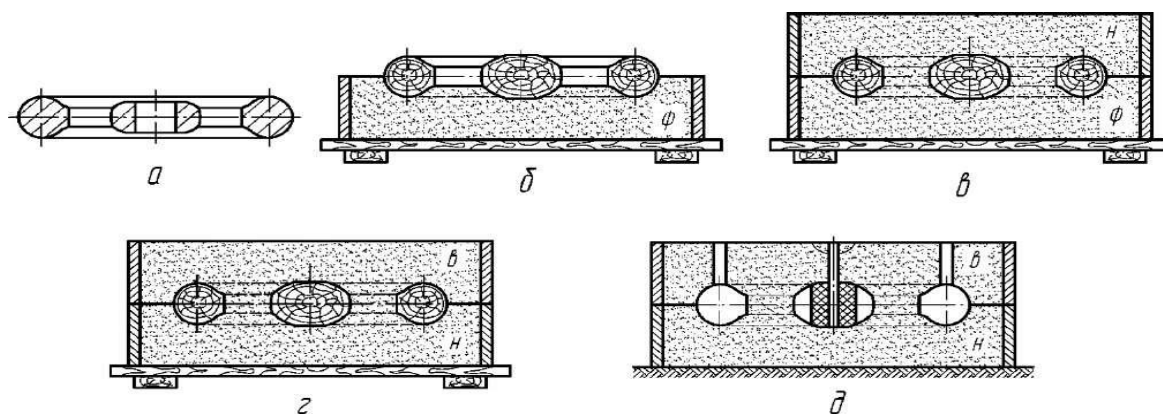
Формовка с фальшивой опокой: *а* - деталь; *б*, *в*, *г* - операции формовки
